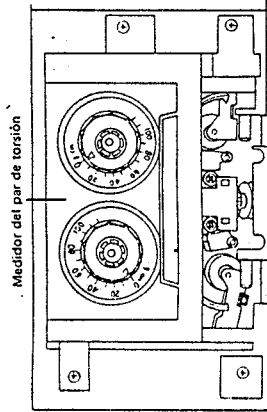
Ajuste del par motor de bobinado en el modo de reproducción
